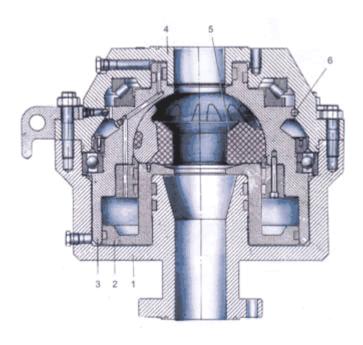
Превентор универсальный вращающийся 1-корпус; 2-поршень; 3-опора; 4-крышка; 5-уплотнитель; 6-шариковый замок
